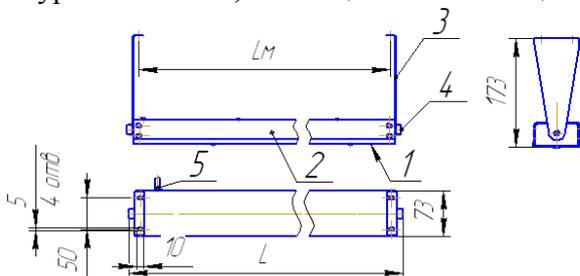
Габаритный чертеж электрообогревателя панельного типа
